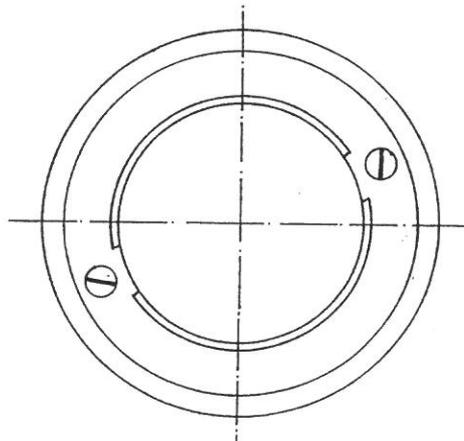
Montage des Rotors (Kolben sind im OT)
